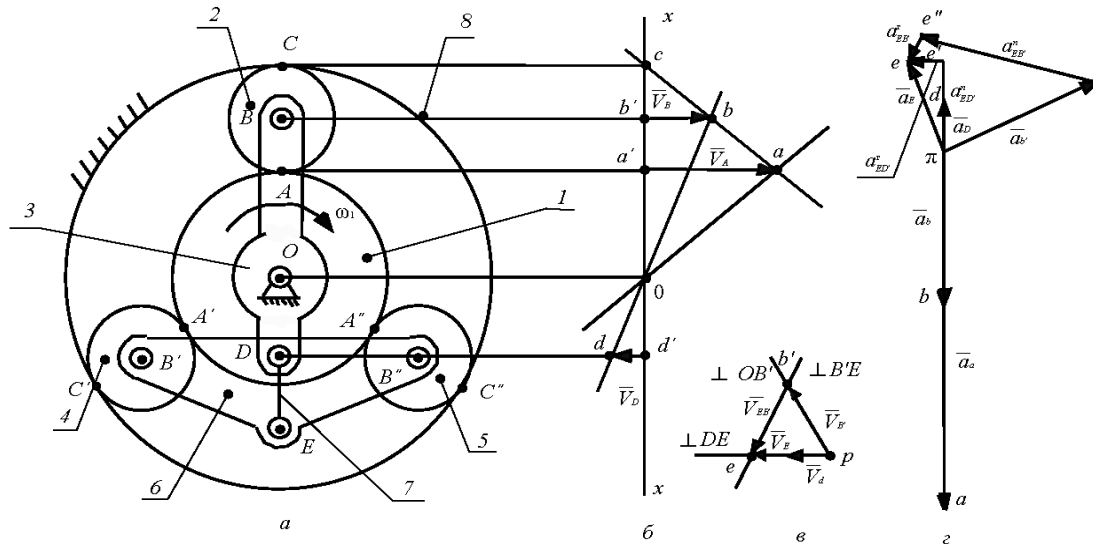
Самоустанавливающийся трехсателлитный планетарный механизм и его кинематическое решение: 1 – подвижное колесо; 2 – спутник; 3 – водила; 4 и 5 – пассивный спутник; 6 – трехпарное звено; 7 – шатун; 8 – неподвижное центральное колесо
